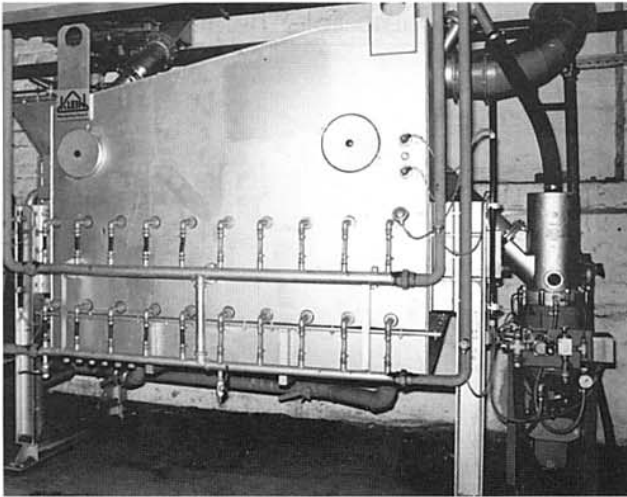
Förderer zum Abtransport von gekühltem Altsand (Typ SP 25, Werkbild Kunming Machine Tool)
